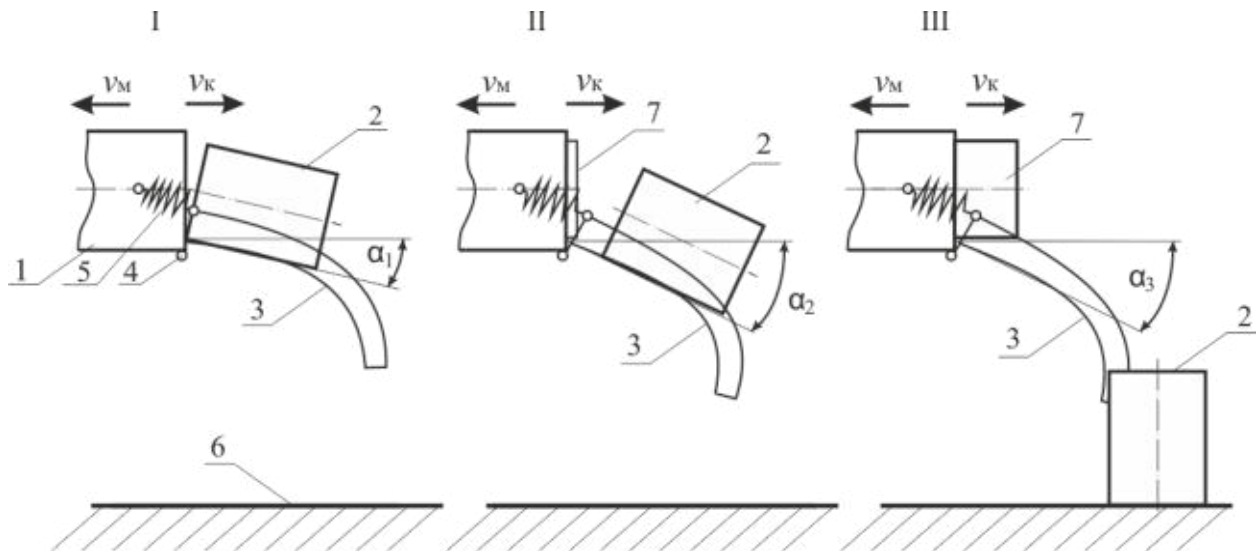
Сопровождение движения торфяного трубчатого куска подпружиненным укладчиком: 1 – мундштук пресса; 2 – трубчатый кусок; 3 – подпружиненный укладчик; 4 – шарнир укладчика; 5 – пружина; 6 – поверхность поля; 7 – выход следующего куска из мундштука пресса
